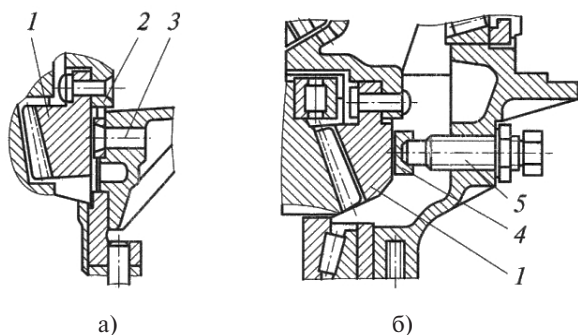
Конструкция упоров ведомой конической шестерни главной передачи: *а* — не регулируемый упор; *б* — регулируемый упор; 1 — шестерня; 2 — пластина; 3 — штифт; 4 — наконечник; 5 — регулировочный болт
